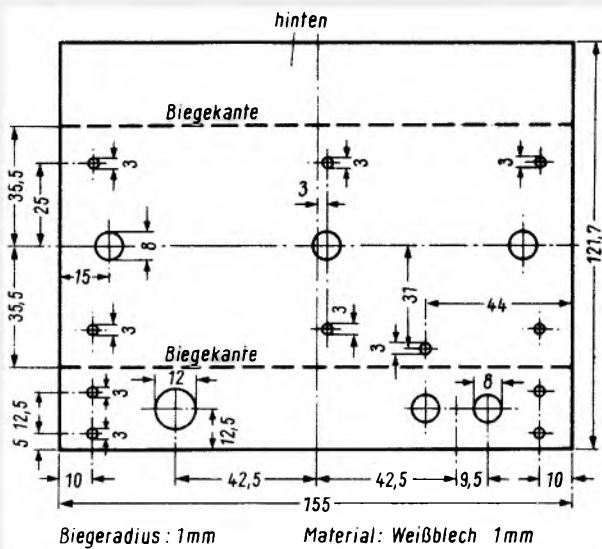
Abwicklung des U-förmigen Chassis mit Bohrungen
